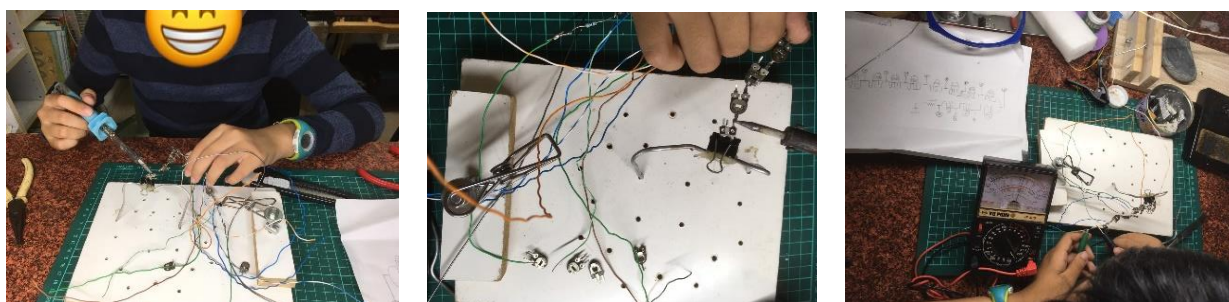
捨棄 PCB 板，改用電線焊接
